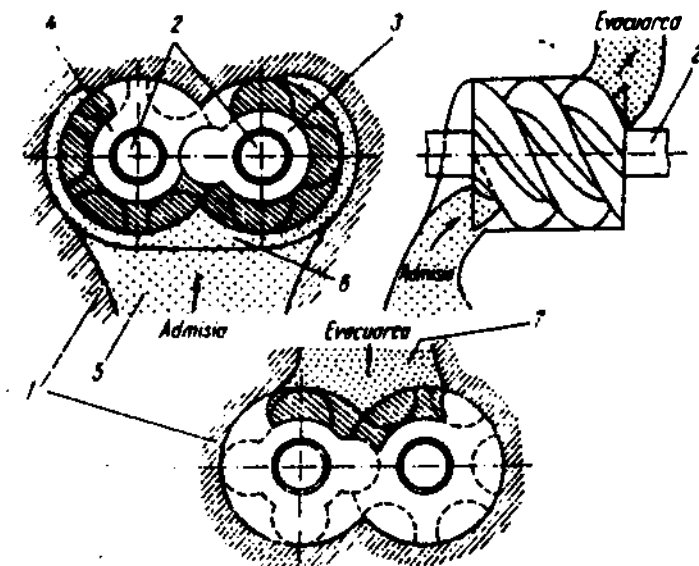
Compresor elicoidal, principiul de funcționare.
